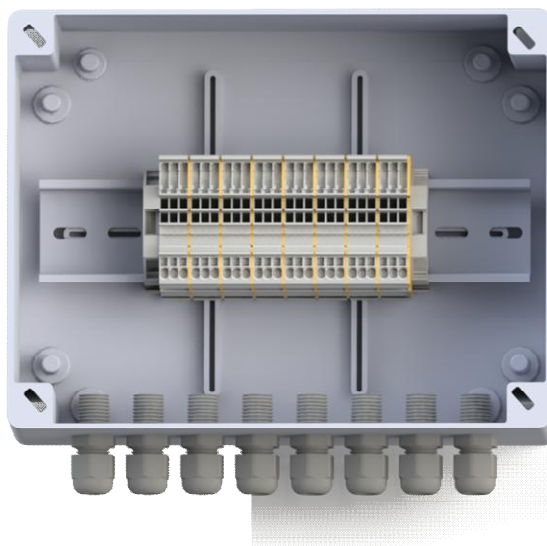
Общий вид ящика подключения ручного считывателя ЯП-01-XX
